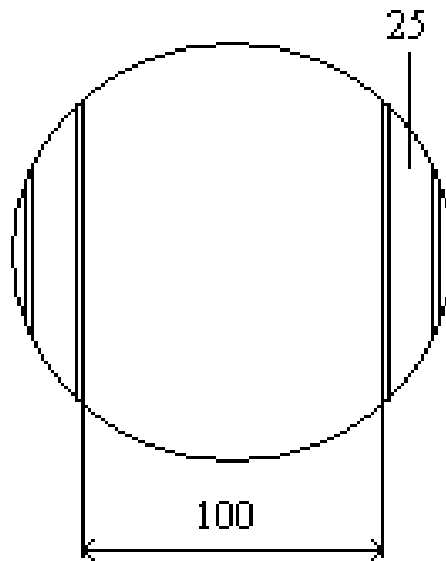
Схема розкрою лісоматеріалу круглого на необрізні пиломатеріали та брус (I прохід)
